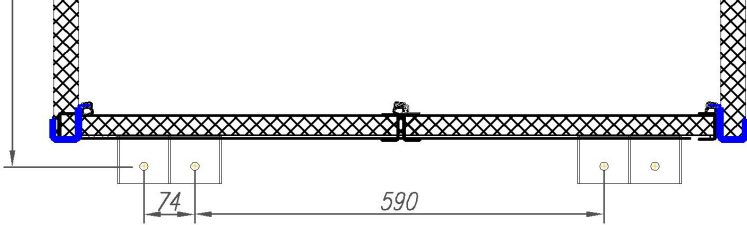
схема монтажа шкафа ТШВП-18106 на бетонное основание.
